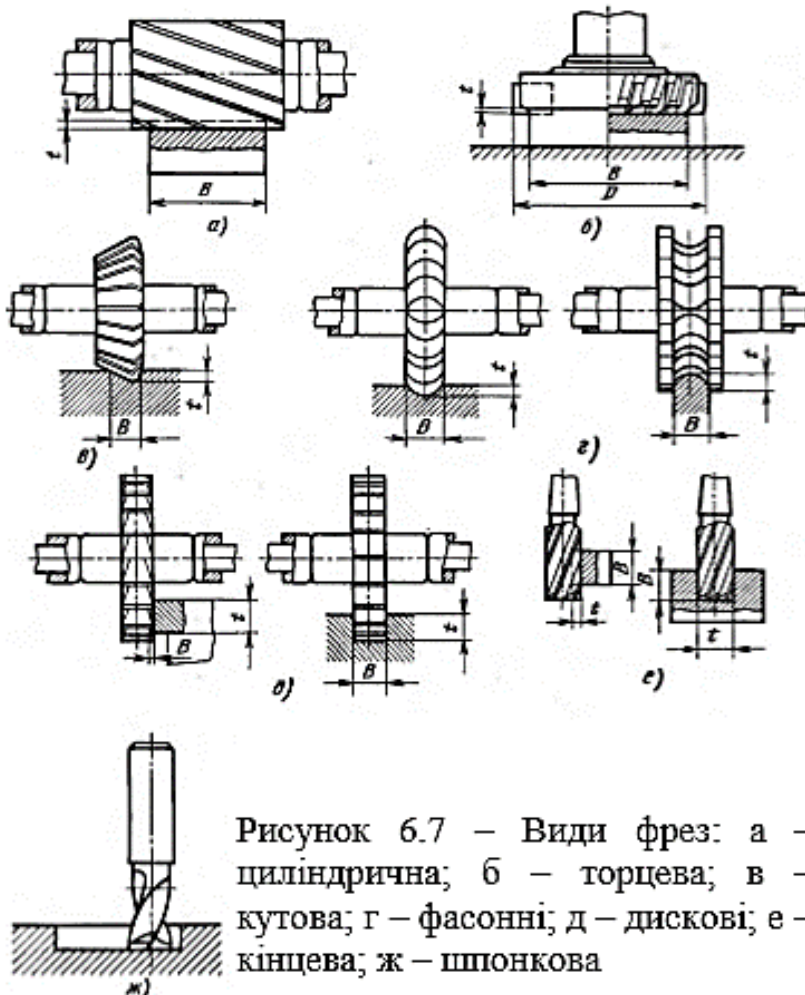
Види фрез: а – циліндрична; б – торцева; в – кутова; г – фасонні; д – дискові; е – кінцева; ж – шпонкова
